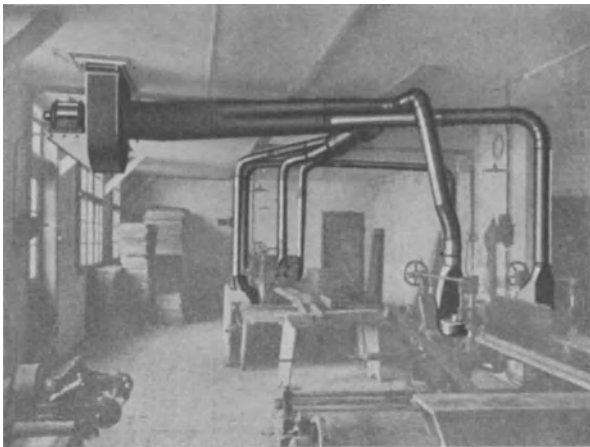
Absaugung von Spänen einer Hobelmaschine.
